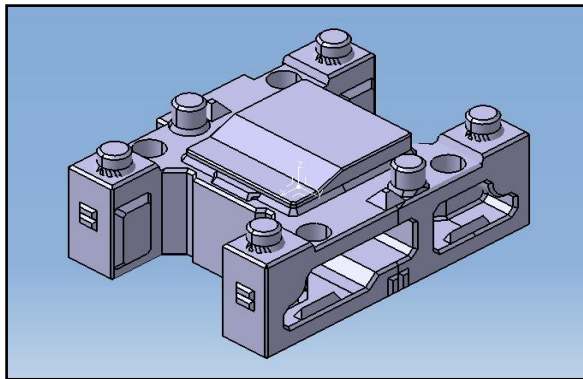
ชิ้นงานโม่ทั้ง 3 ชิ้นที่นำมา ASSEMBLY เหมือนการ
